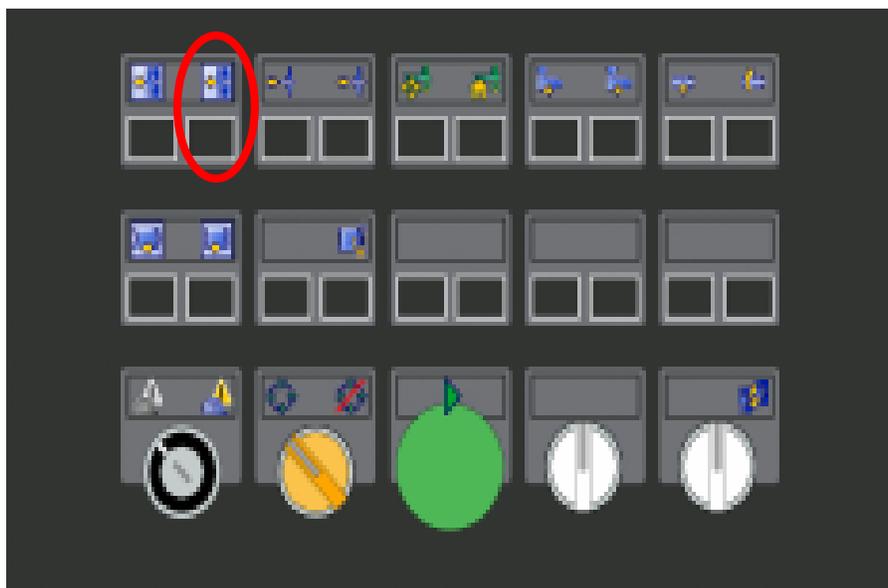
(operator manual machine duo 7050/1900 WP US ENGEL, 2013)
